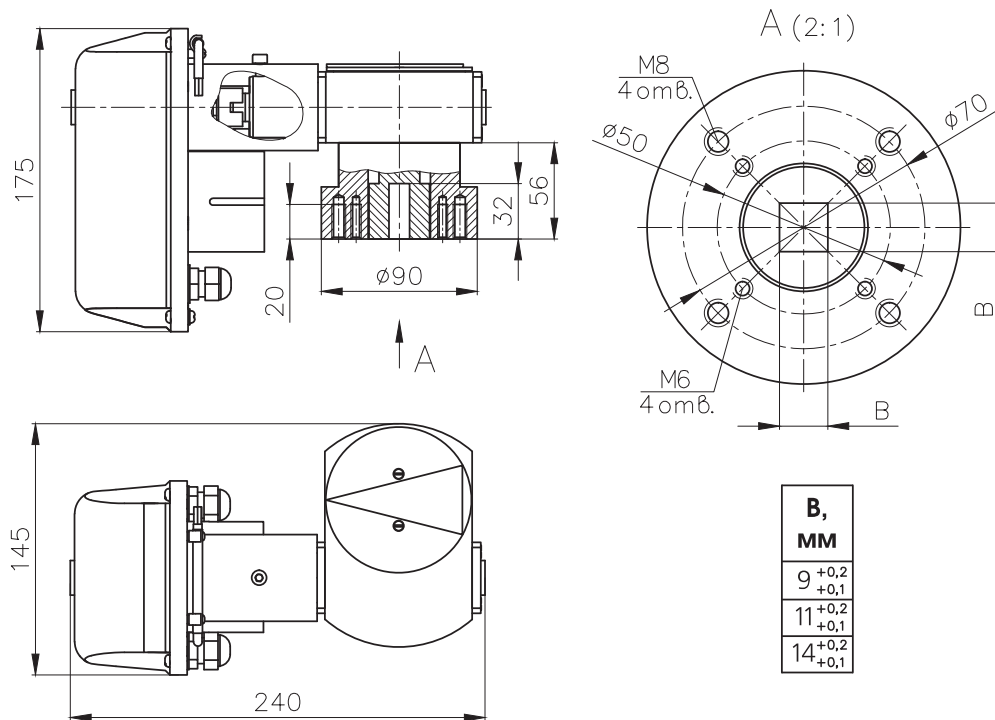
Габаритные и присоединительные размеры ЭИМ
